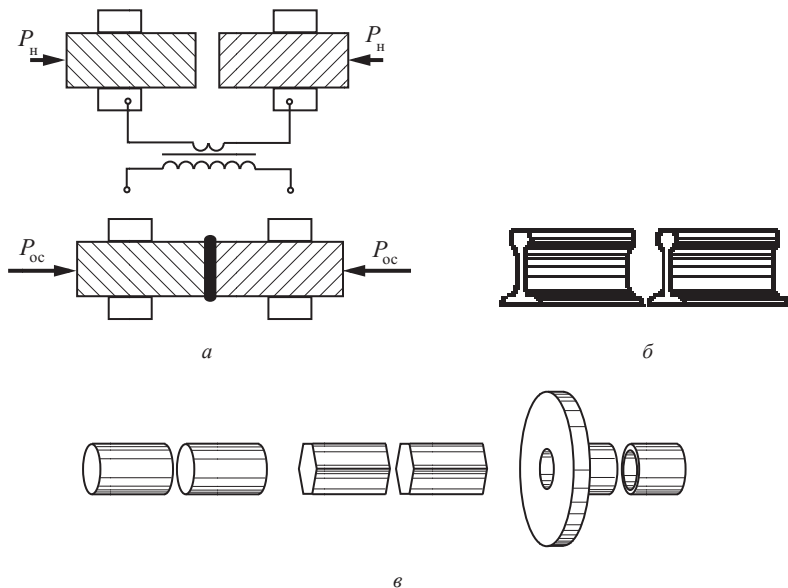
Стыковая контактная сварка: *а* – стадии контактной сварки сопротивлением; *б* – типы сварных соединений сварки оплавлением; *в* – типы сварных соединений сварки сопротивлением
